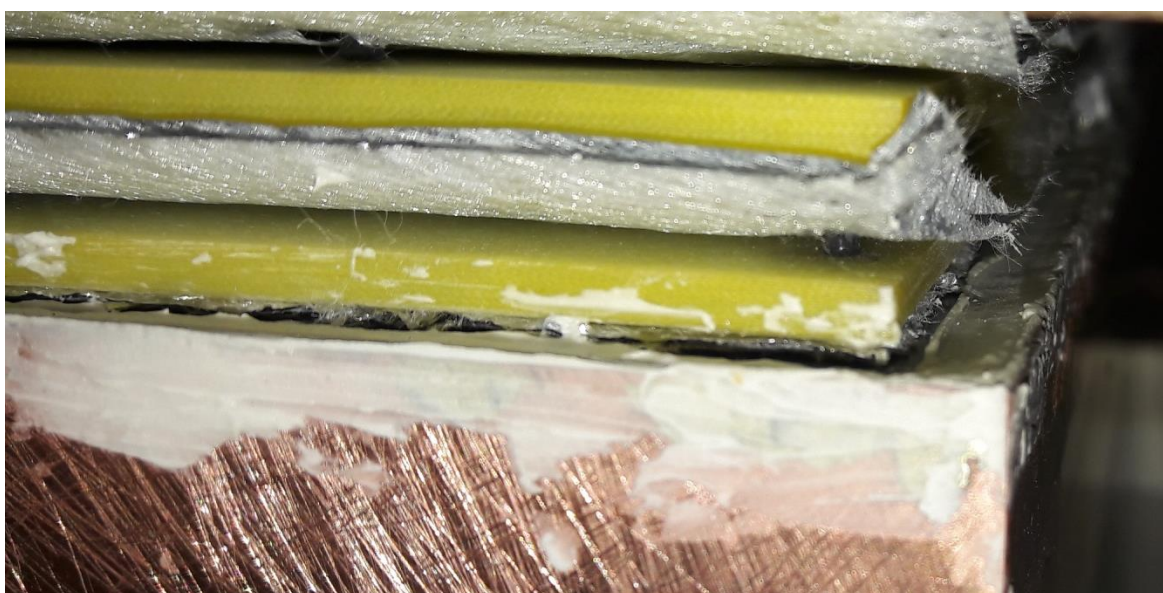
Aplicação da resina EP21TCHT-1 para fechar micro trincas na solda
